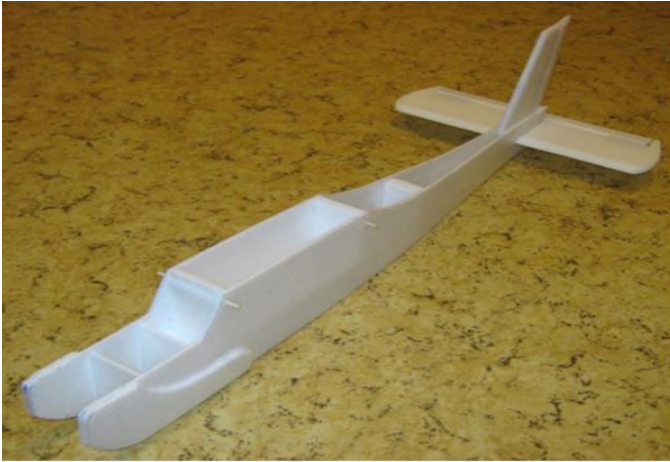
Изготовление киля и руля высоты. Фото автора.
